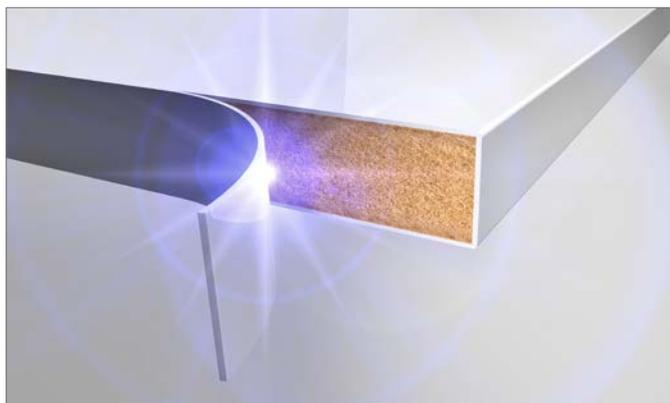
Canteado sin juntas – RAUKANTEX visions pro
